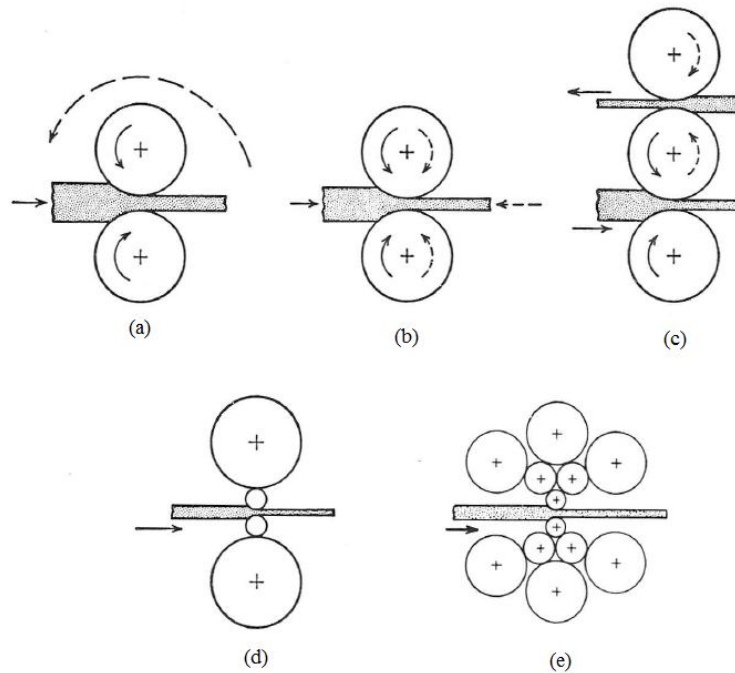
Arranjos típicos de rolos/cilindros para laminadores. (a) Laminador duo; (b) laminador duo reversível; (c) laminador trio; (d) laminador quádruo; (e) laminador agrupado [22].
